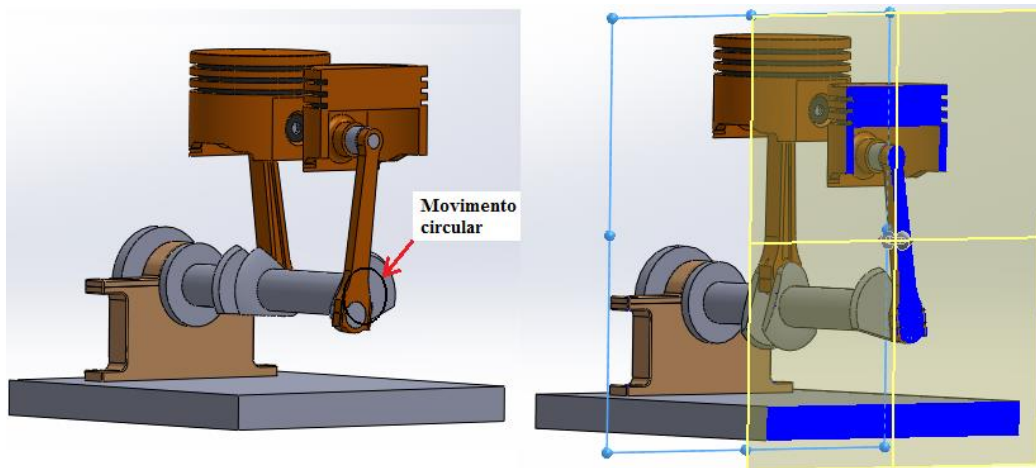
Exemplo de um movimento de manivela (embolo e haste).
